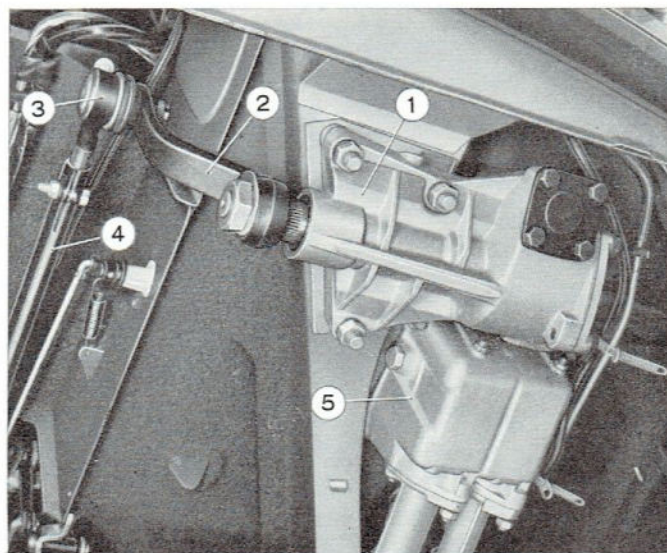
Ansicht des Lenkgehäuses am Fahrzeug.
